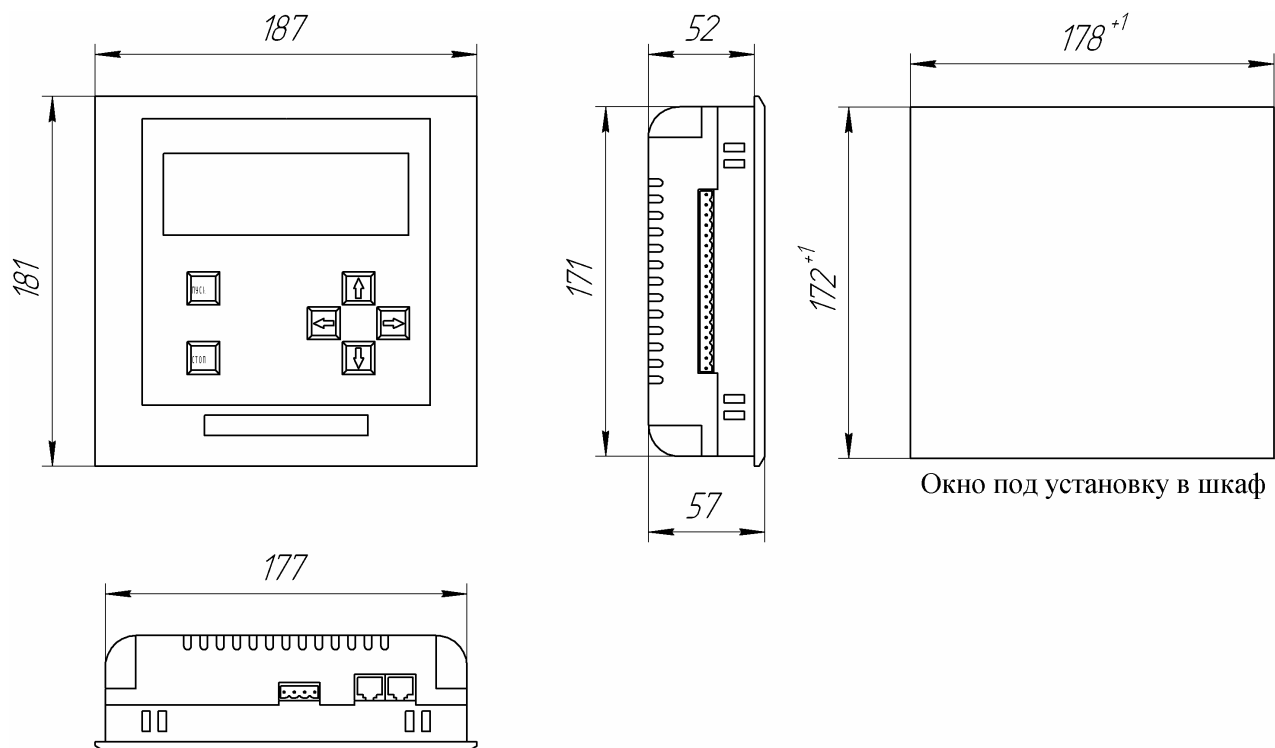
Габаритные размеры БАУ «ВЕГА-10» версии 2.3.
